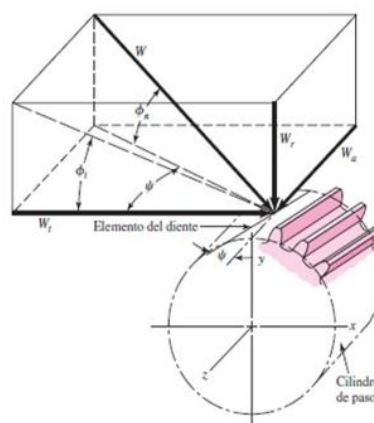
Fuerzas generadas por un engranaje helicoidal
